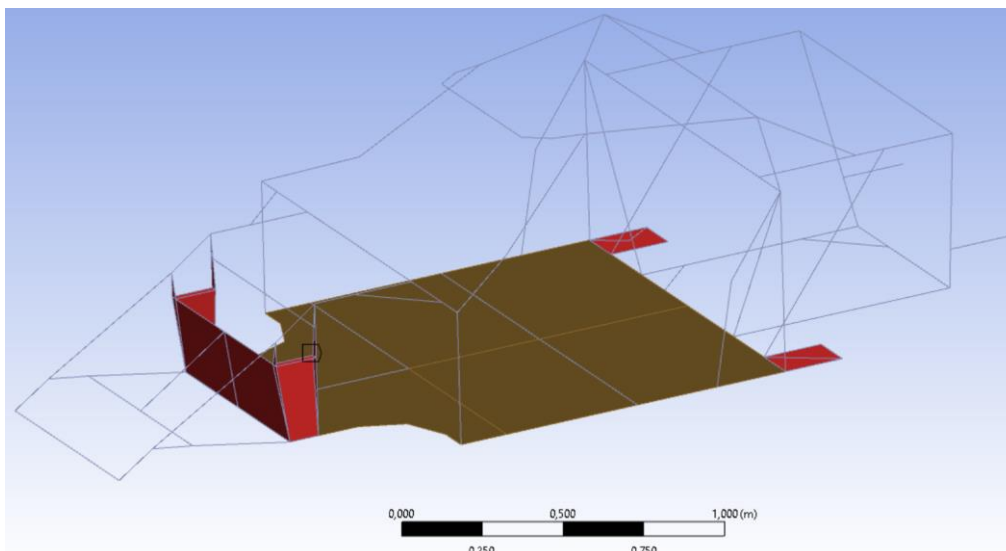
Atribuição do Aço Estrutural a determinadas placas da estrutura.
